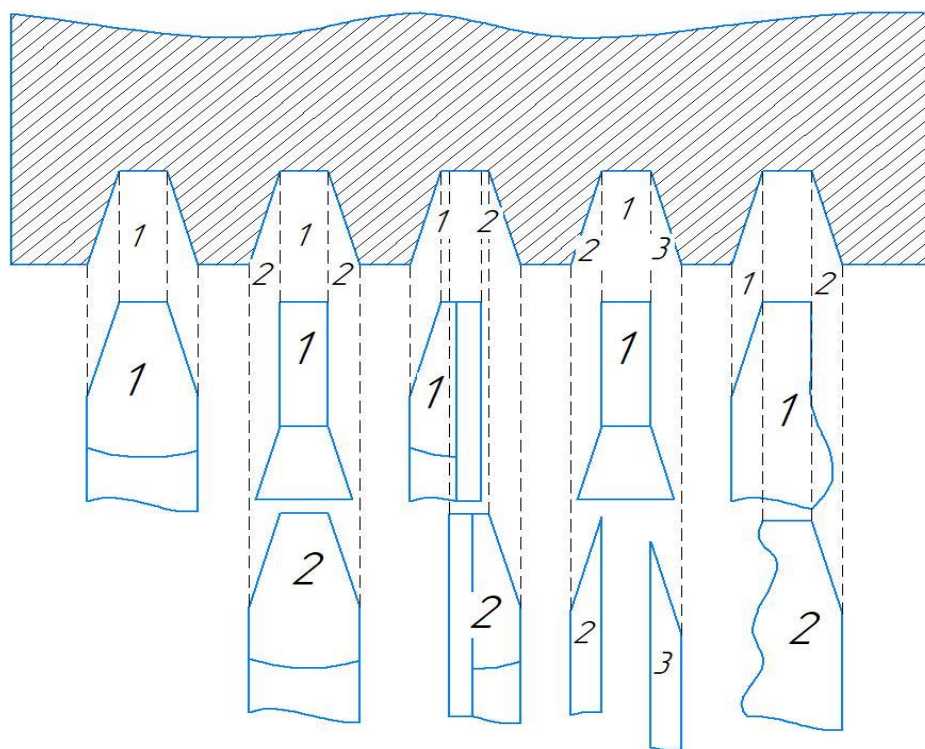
Схема образования резьбы резцами полного и разделного профиля
